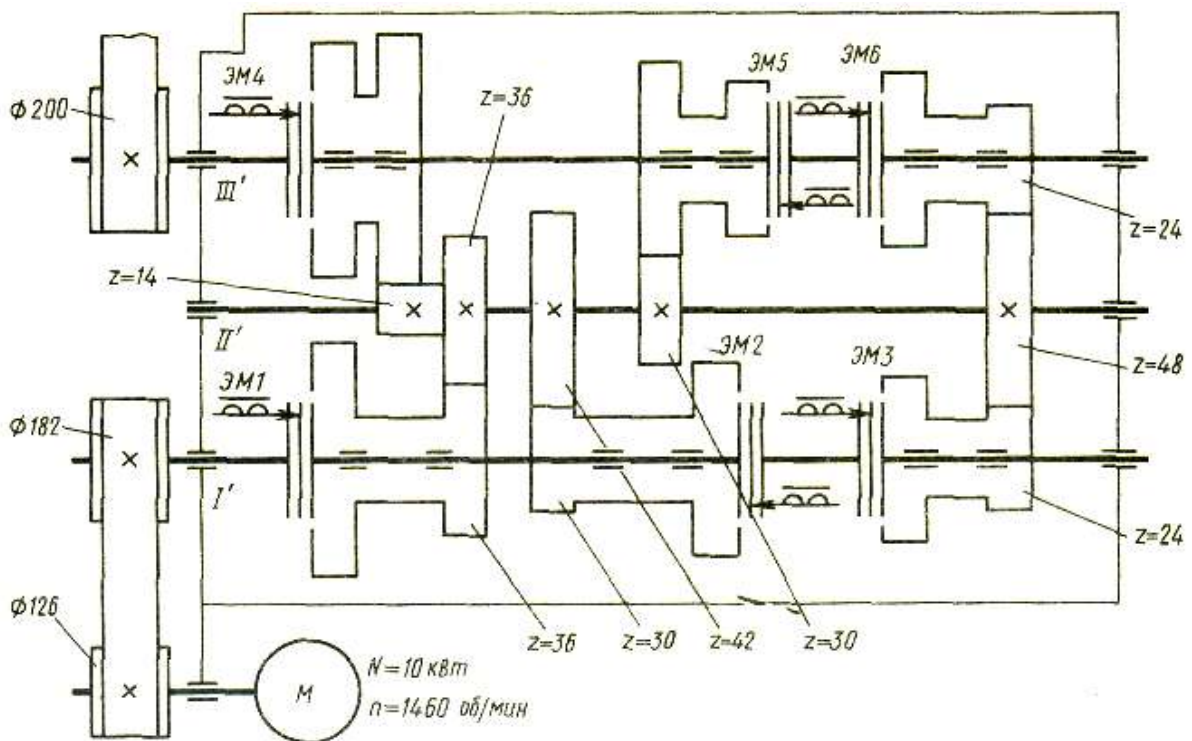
Схема автоматичної коробки швидкостей
